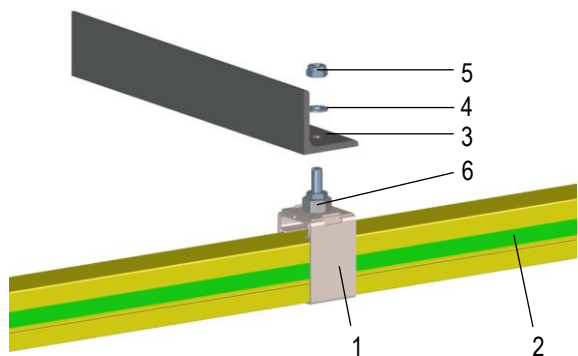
Montage du profil ProfiDAT® sur une structure de maintien
